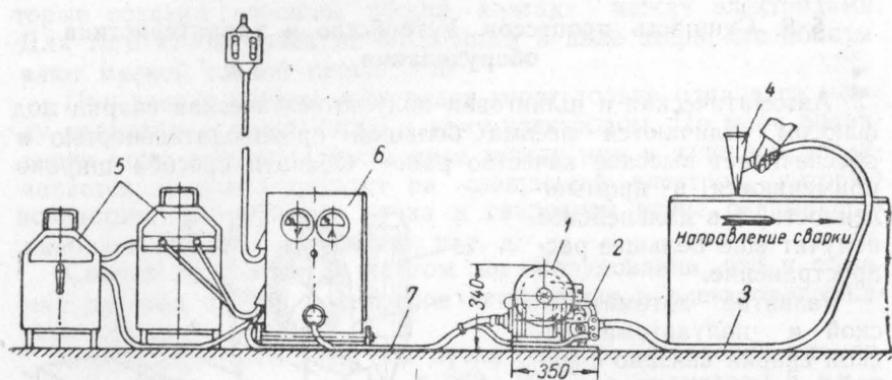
Схема автоматической сварки под флюсом:
